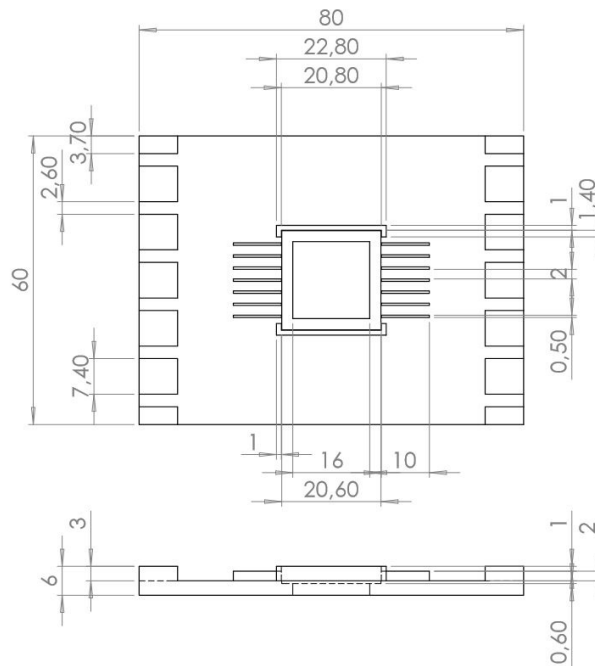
Primer diseño del porta-prototipo. Todas las dimensiones se expresan en milímetros.
